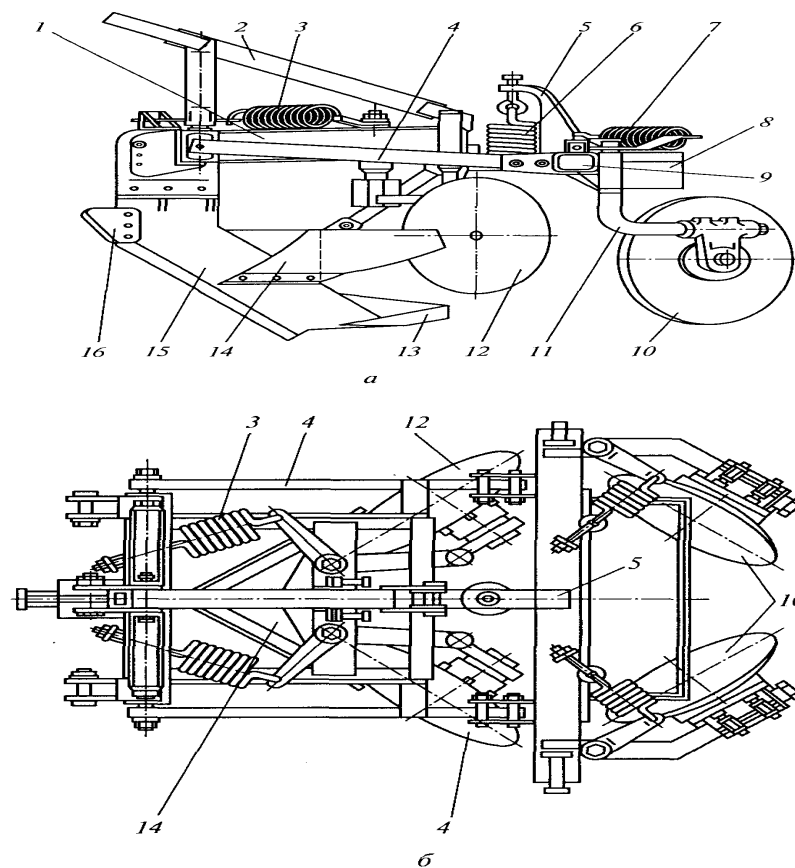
Плуг лесной дисковый ПЛД-1,2: *а* — вид сбоку; *б* — вид сверху;
